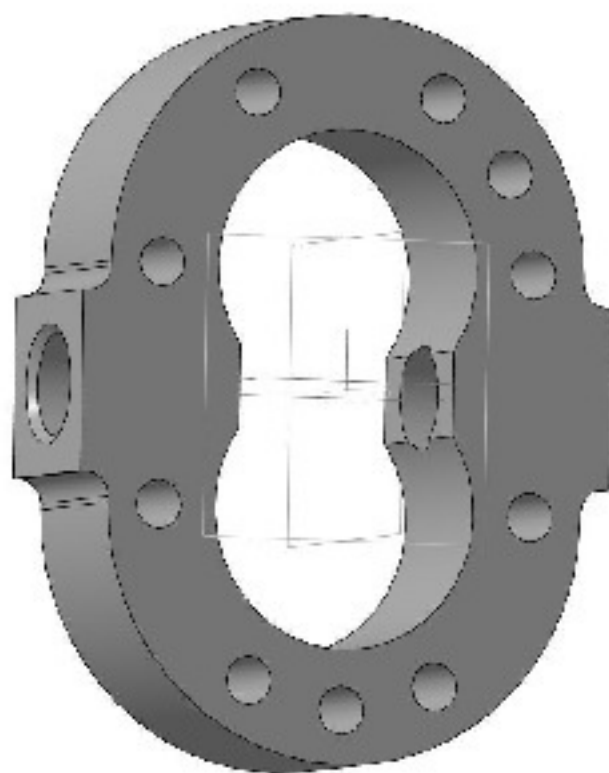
3D-модель деталі «Корпус шестеренного насоса»
